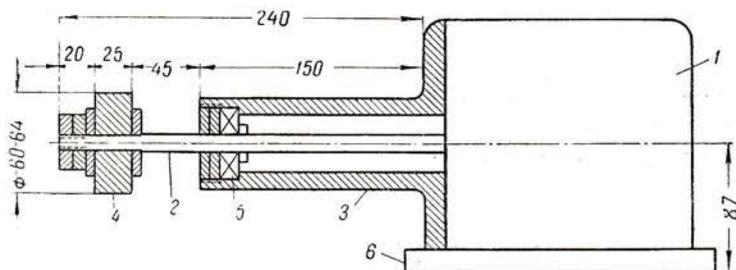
Агрегат для шлифовки цилиндров двигателей на токарном станке
